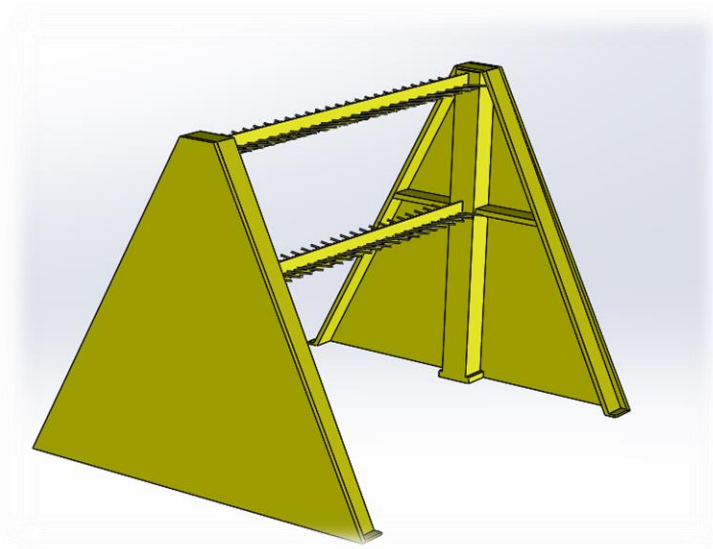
Desenho em *SolidWorks*® da estrutura para suporte dos raios
